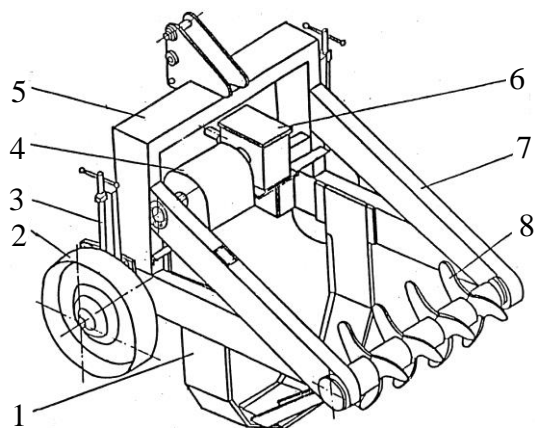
Корчеватель непрерывного действия КНД-1,1:
